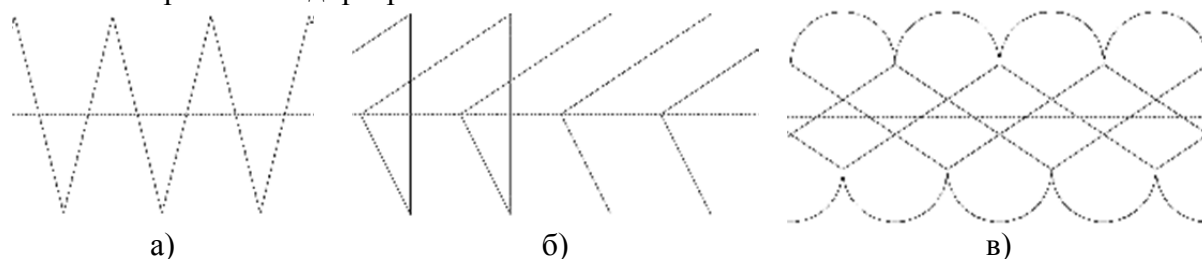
Фрагменты траектории осцилляций сварочной горелки
